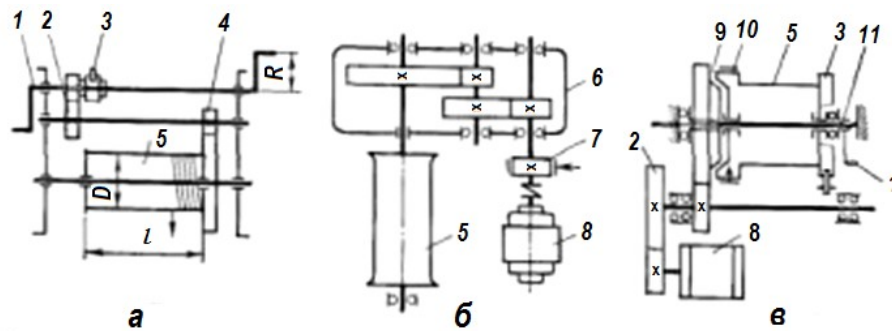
Схеми лебідок: а – з ручним приводом; б – електрореверсивна; в – фрикційна;
